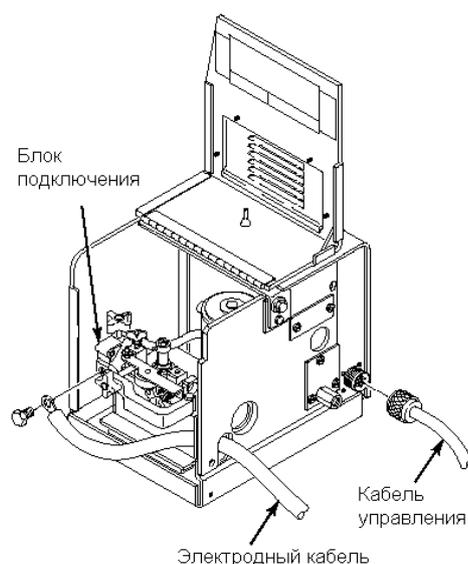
Подключение входного сварочного и кабеля управления.
